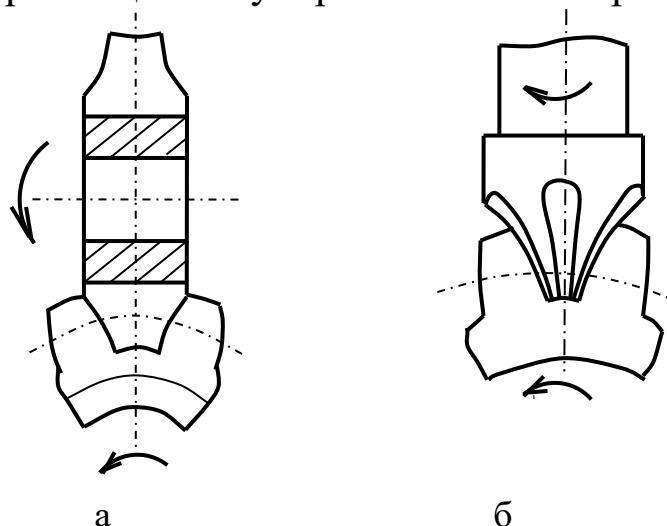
Схема нарізання зубчастих коліс модульними фрезами
